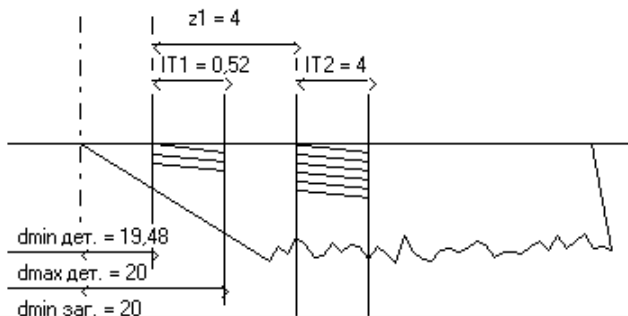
Схема расположения припусков, допусков и межоперационных размеров
